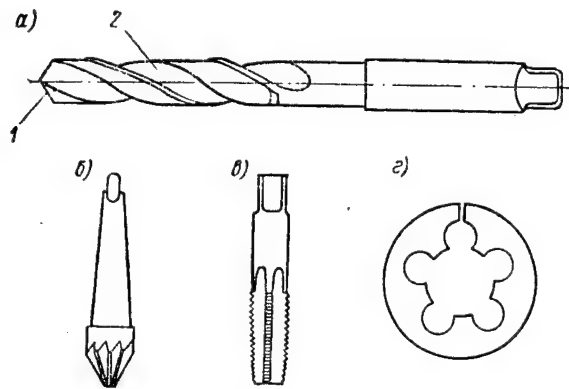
Инструмент для сверления и обработки отверстий: а — спиральное сверло; б — коническая зенковка; в — метчик; г — плашка.
